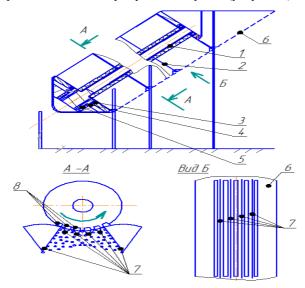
Схема дискового режущего аппарата 1 — вал; 2 — диск; 3 — манжета; 4 — звездочка; 5 — подшипник; 6 — передняя стенка; 7 — делитель; 8 — противорез
